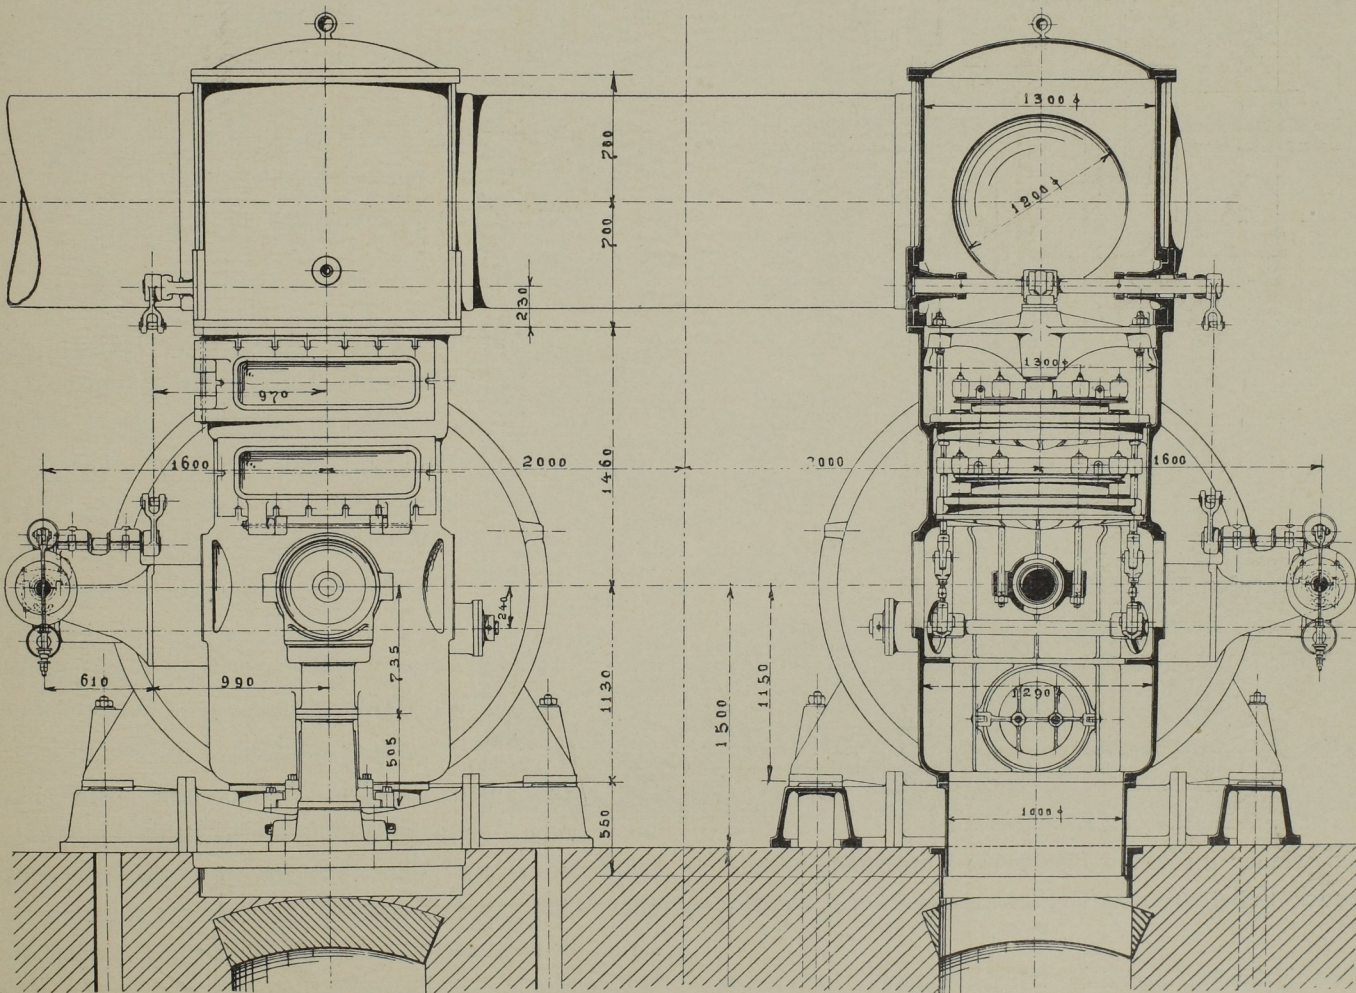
Stirnansicht und Schnitt der Windcylinder. Massst. 1:40.
